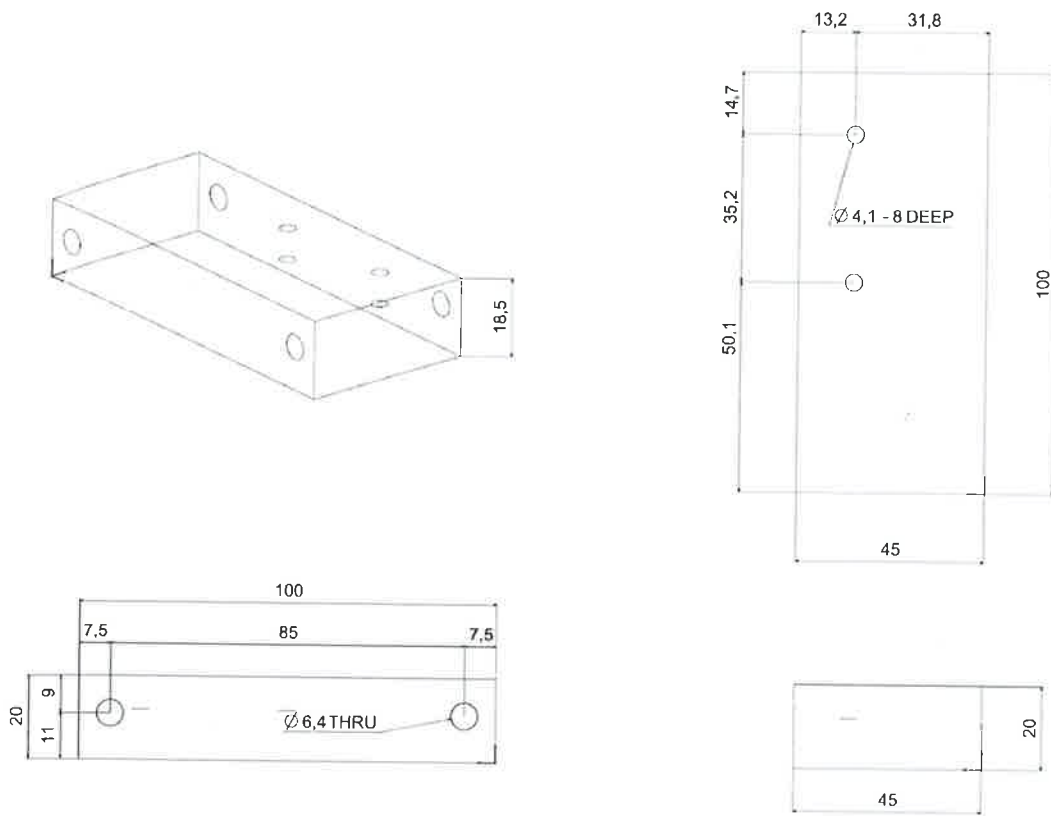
Perspectiva trimétrica, superior, frontal e izquierda del soporte para el motor
